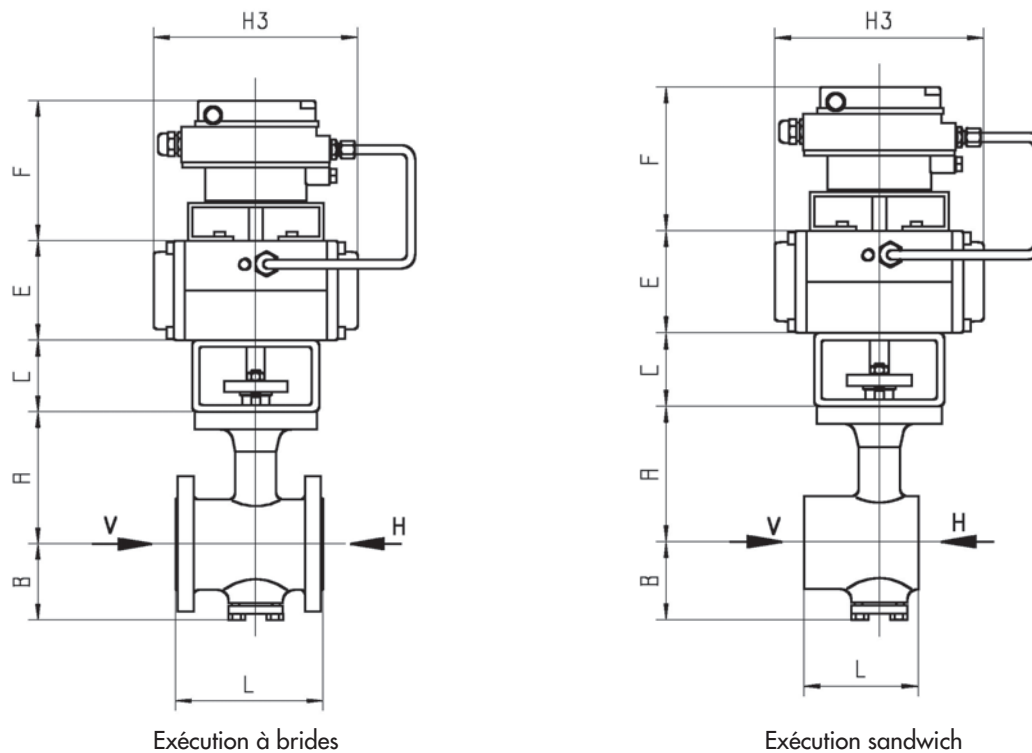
· Dimensions vanne VETEC type 72.3/AT et VETEC type 72.4/AT
